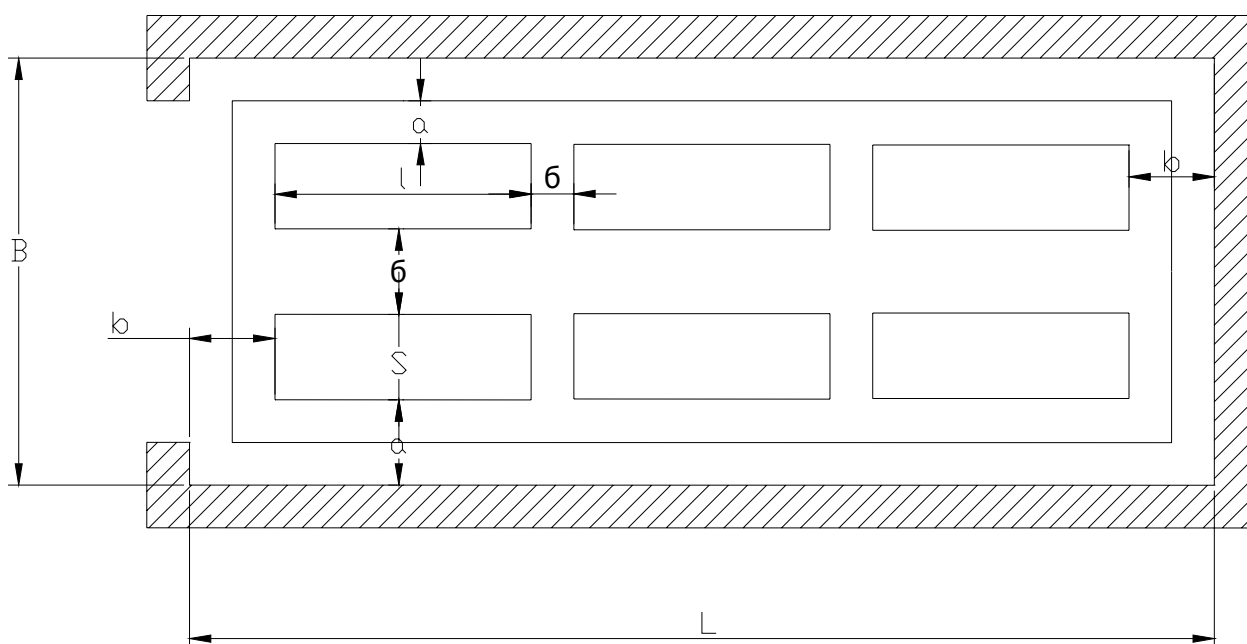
Вид камерной печи сверху с продольным расположением заготовок
